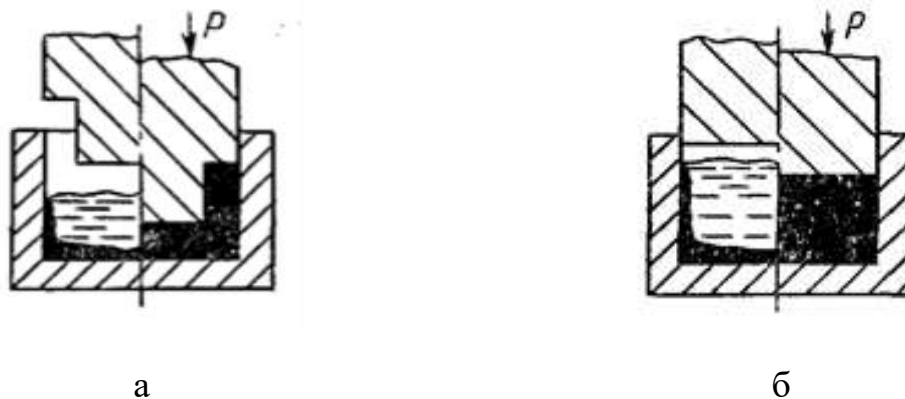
Схема пуансонного (а) поршневого (б) прессования затвердевающих отливок при ЛКД
